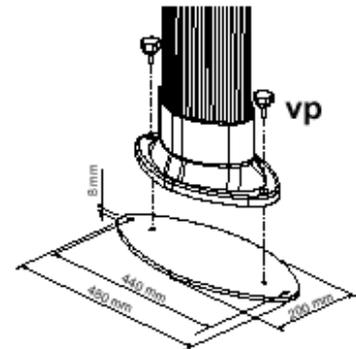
Расположение отверстий для монтажа дополнительных металлических пластин
